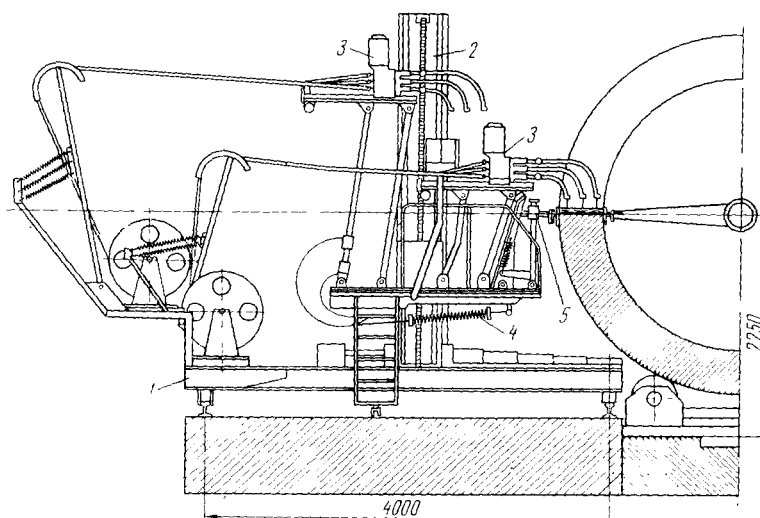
Установка с дублирующими головками для электрошлаковой сварки кольцевых швов:
